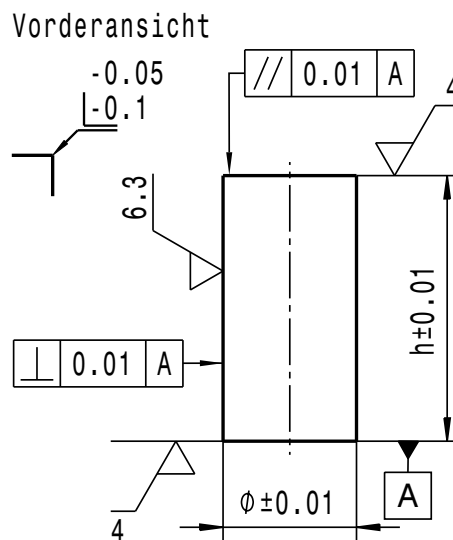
Ausschnitt aus Fertigungszeichnung der Proben mit geschliffener Stirn- und schlichtgedrehter Mantelfläche (Bemaßung in mm)
